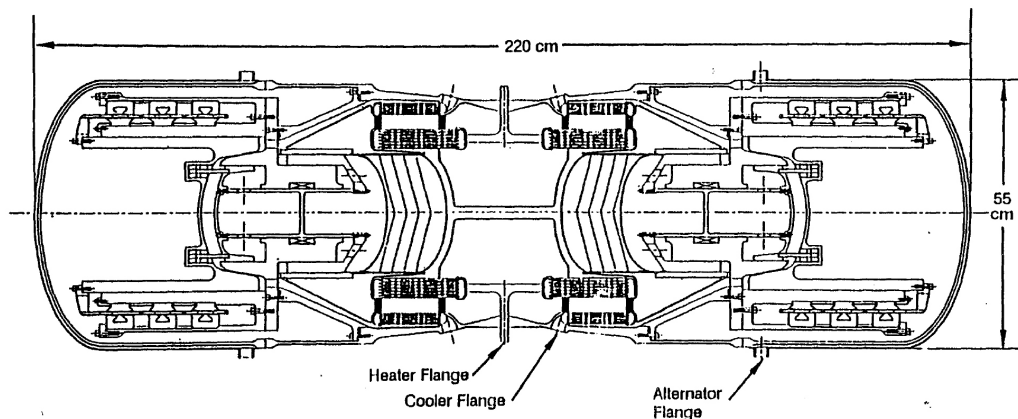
Unità di conversione Free-Piston per il reattore SP-100, composta da due motori in contrapposizione,[11]
